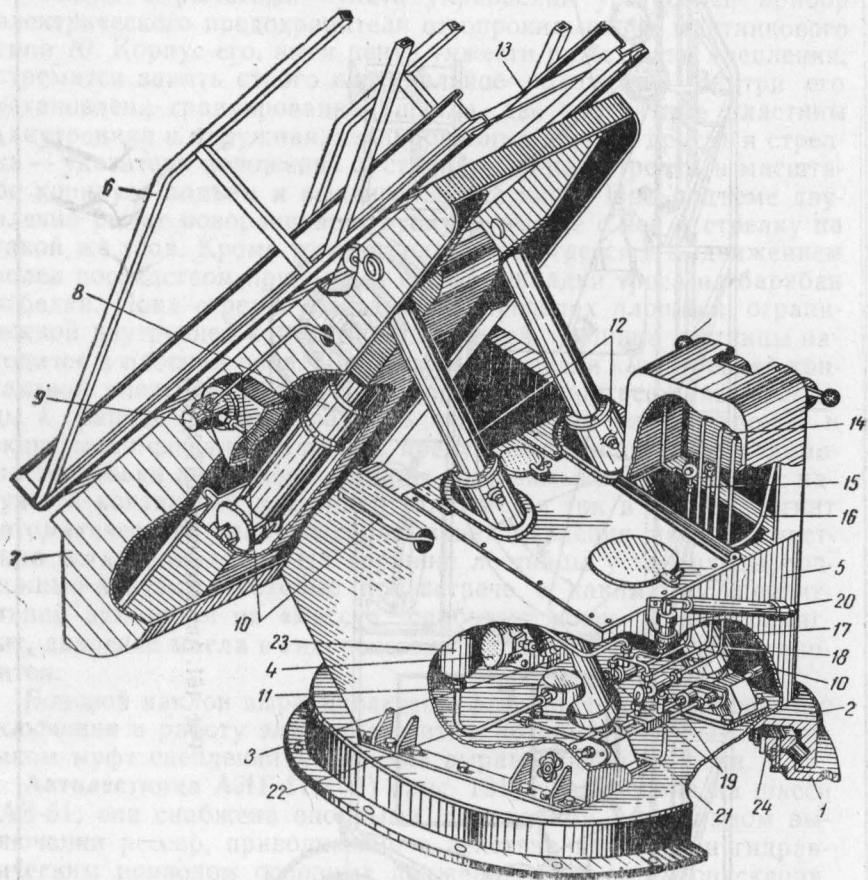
Подъемно-поворотное основание и механизм гидропроводов
